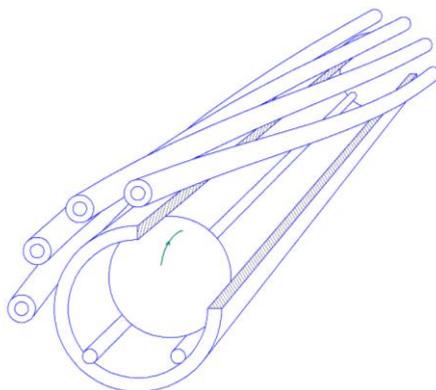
Индуктор в форме цилиндрической винтовой линии
